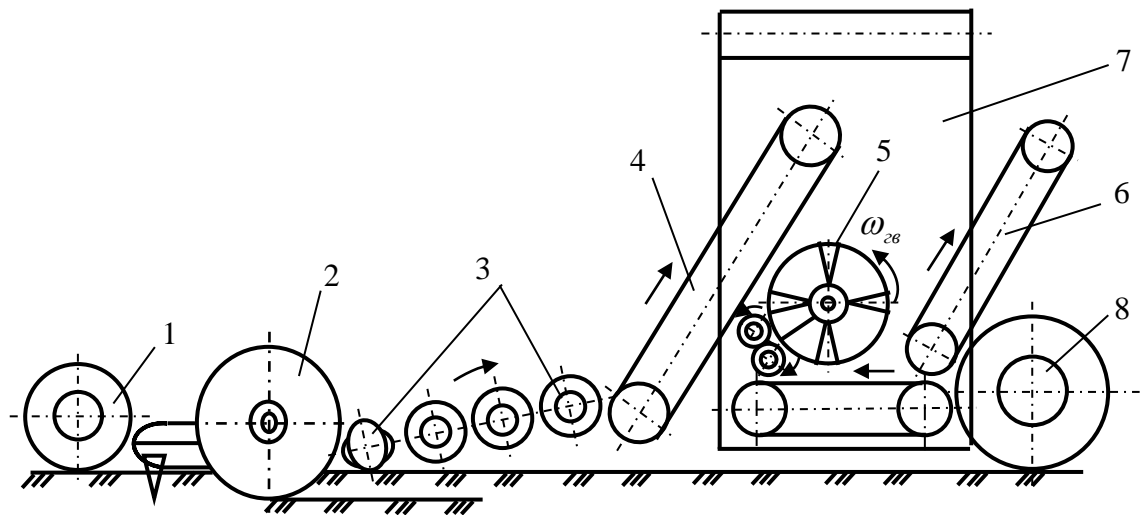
Конструктивно-компонувальна схема модернізованої коренезбиральної машини: 1 – копіювальне колесо; 2 – дисковий сферичний копач; 3 – очисник вороху; 4, 7 – повздовжній і вивантажувальний транспортери;
